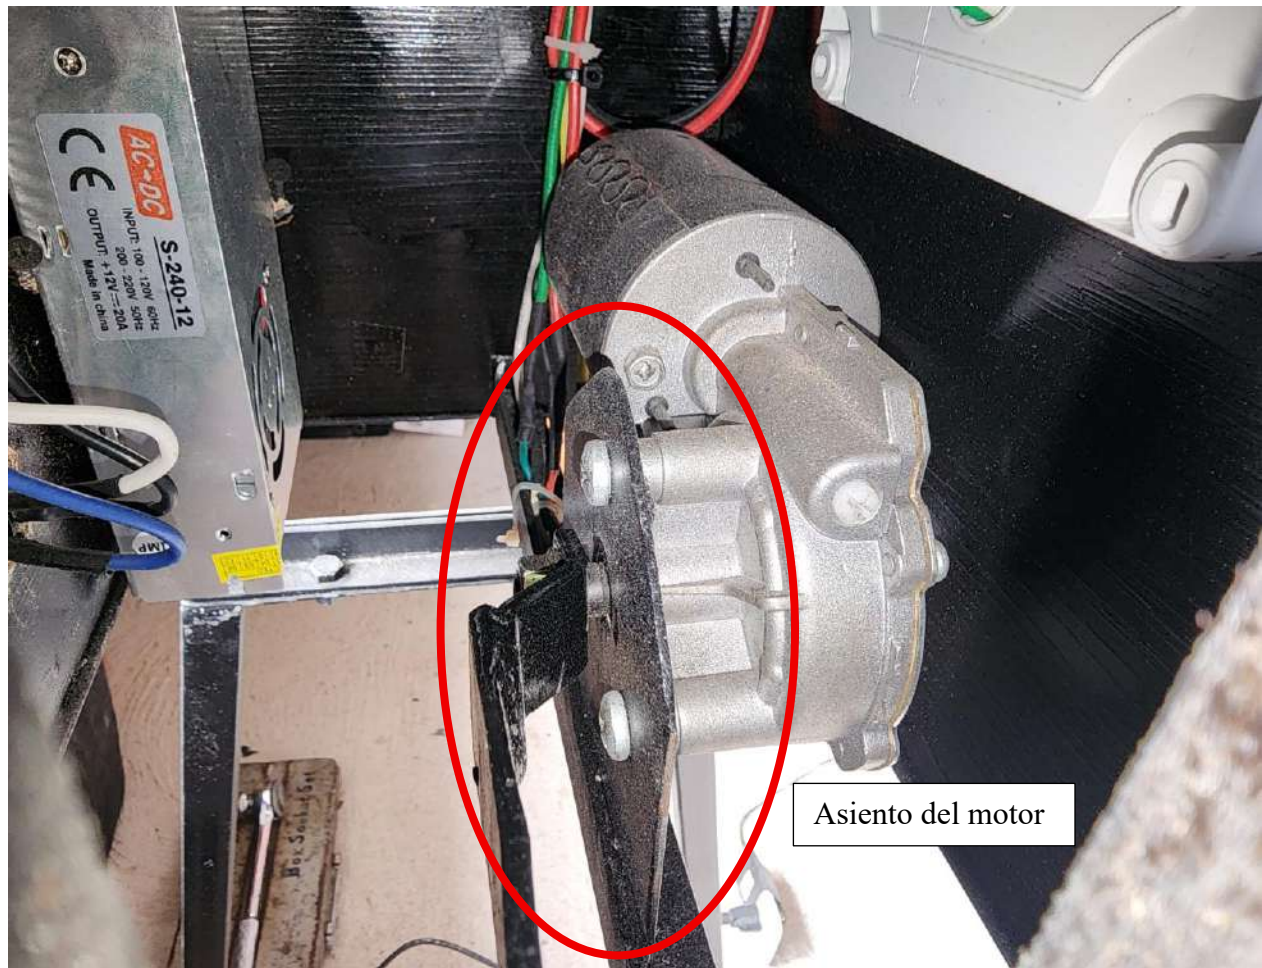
Asiento del motor impulsor del sistema biela-manivela
